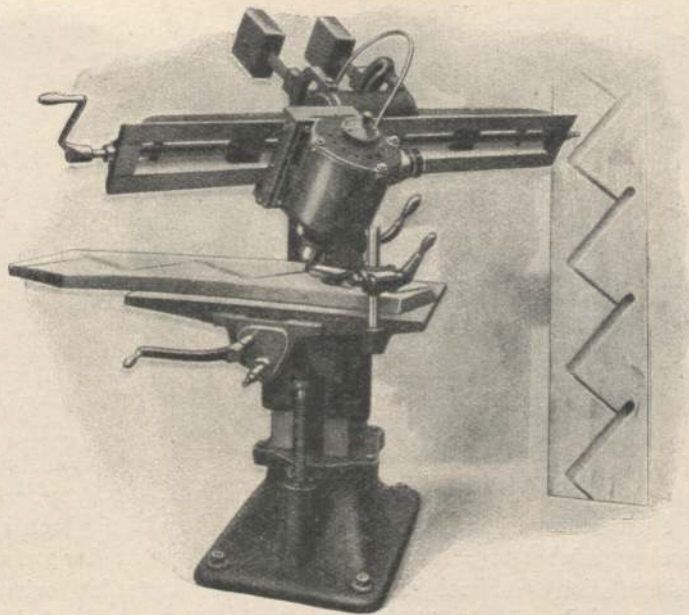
Die einspindelige Treppenfräse mit schräg stehender Spindel und schräg stehendem Motor. Durch die schräge Einstellung des Motors kann man selbst bei gewundenen Treppen unterstemmte oder ausgeflossene Tritt- und Futterbrettlöcher anfertigen.
